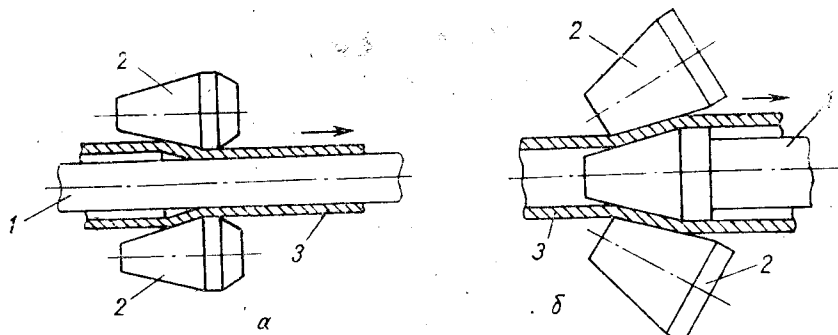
Схеми поперечного прокатування трубчастих заготовок на циліндричній (а) та конічній (б) оправках:
